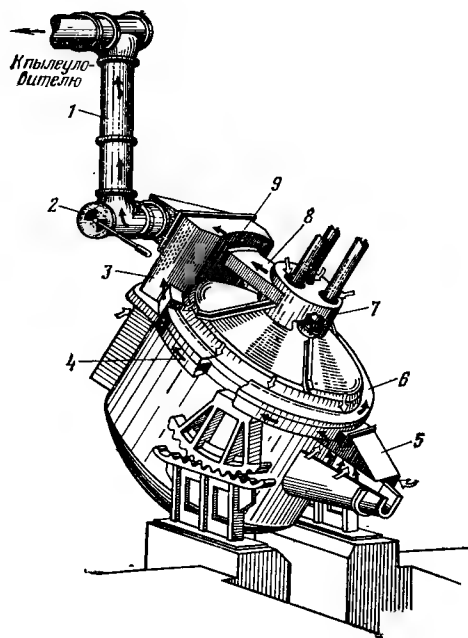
Полностью закрытое вытяжное устройство для дуговой печи (с частыми наклонами для выпуска металла) [621]:
